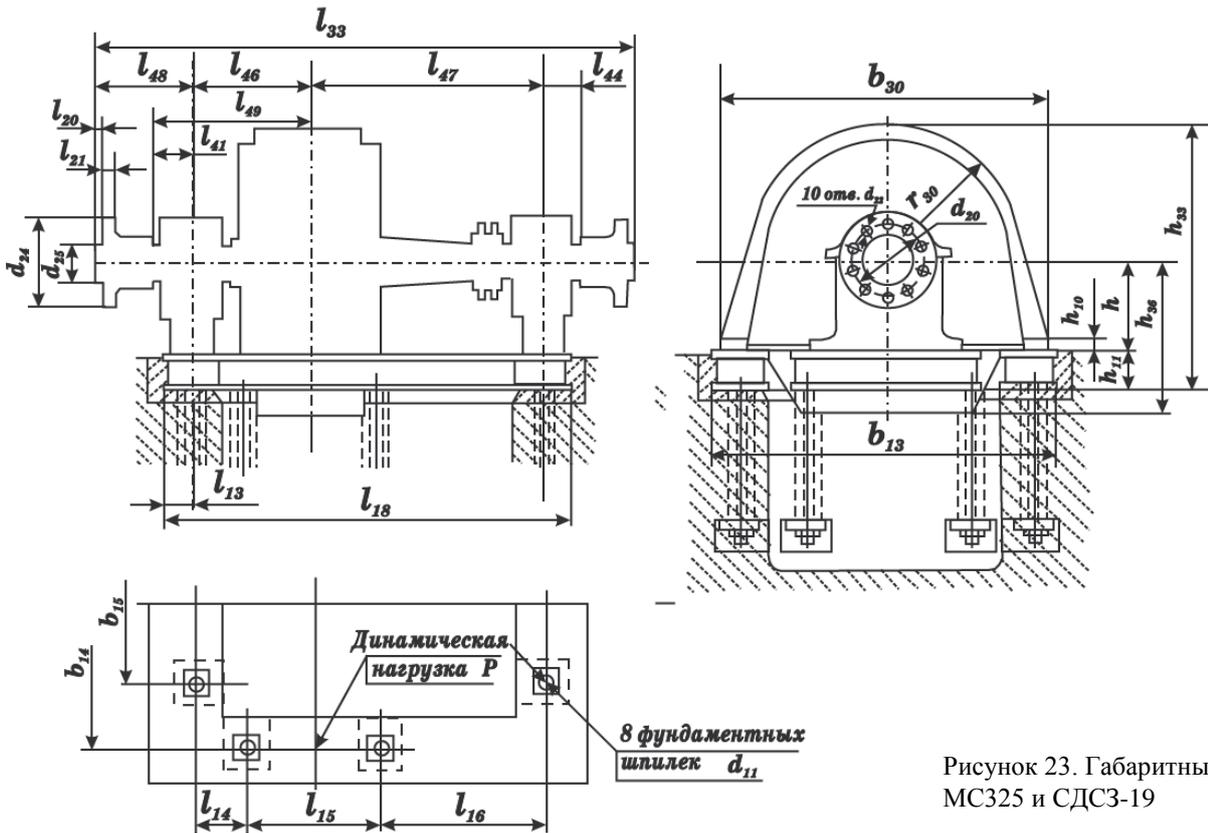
Габаритные размеры МС325 и СДС3-19
